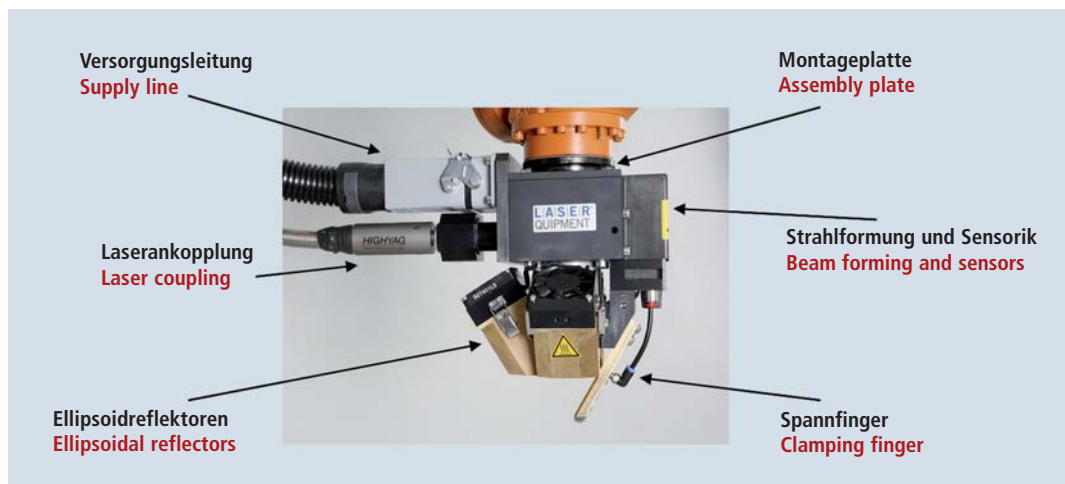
Hybridschweißkopf mit angeschlossenen Versorgungssteckern
